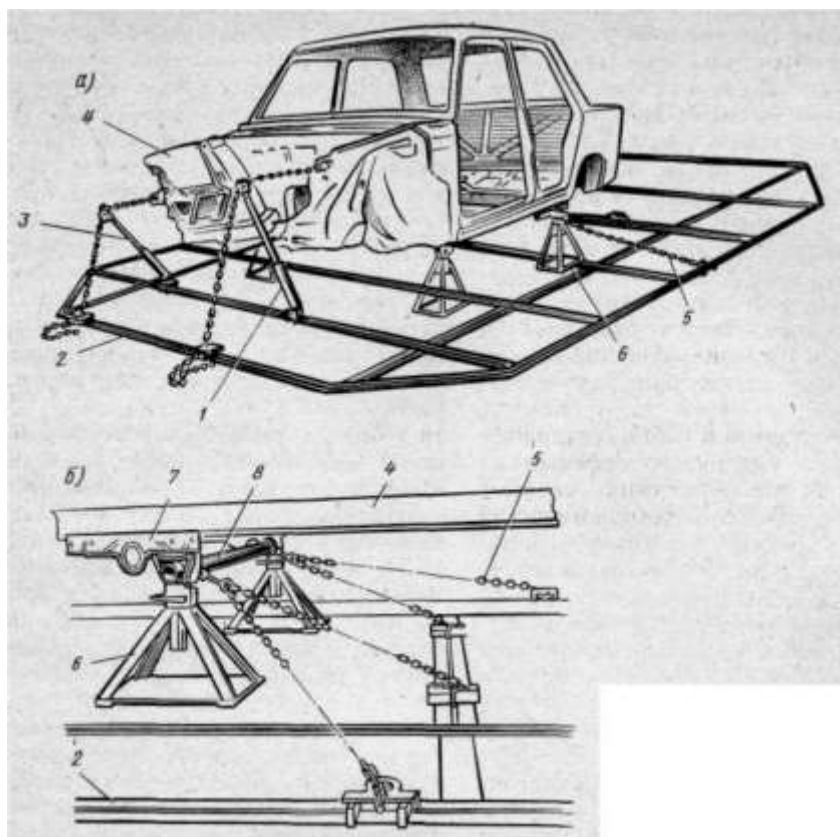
Стационарный стенд для правки кузова легкового автомобиля: *а* — установка кузова на стенде; *б* — крепление кузова при правке
